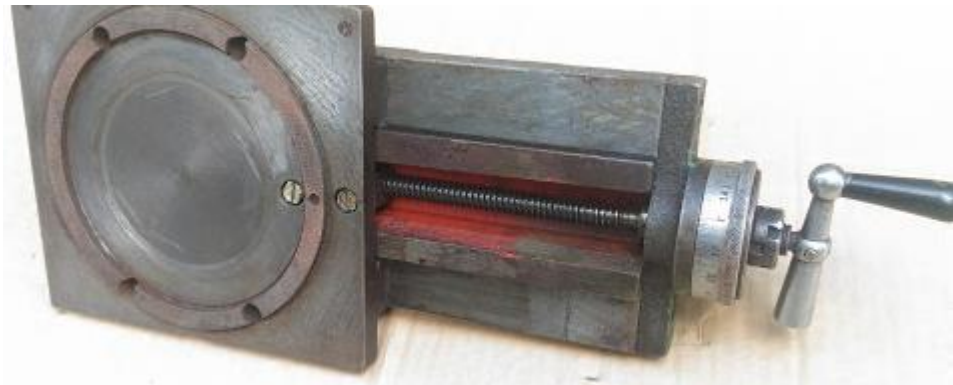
Верхні салазки супорту верстата [36]
